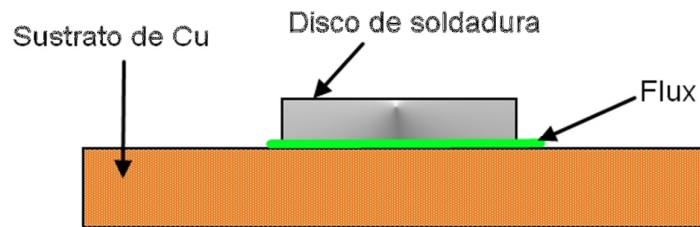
Disco de soldadura, sobre un sustrato de cobre, cubierto de flux soluble en agua.
